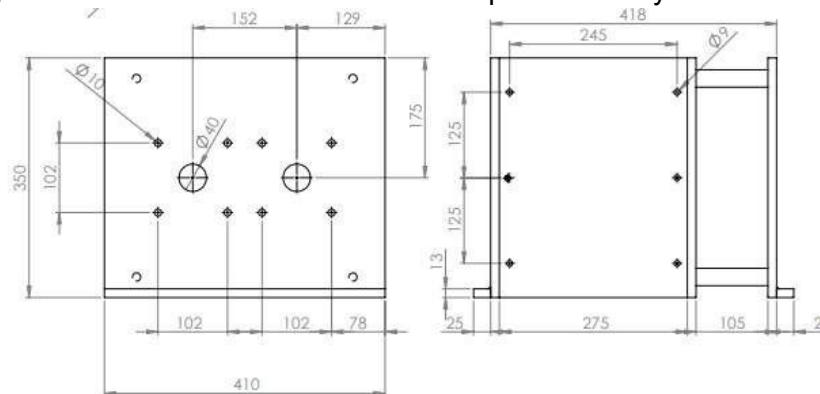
Dimensiones de la trituradora parte frontal y trasversal
